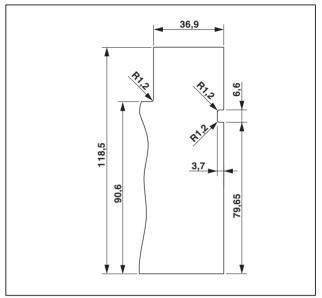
Maßzeichnung der senkrechten Gehäuse-Leiterplatte bei Verwendung der Matrix (2201496) oder der Einlegeplatte (2201497)
